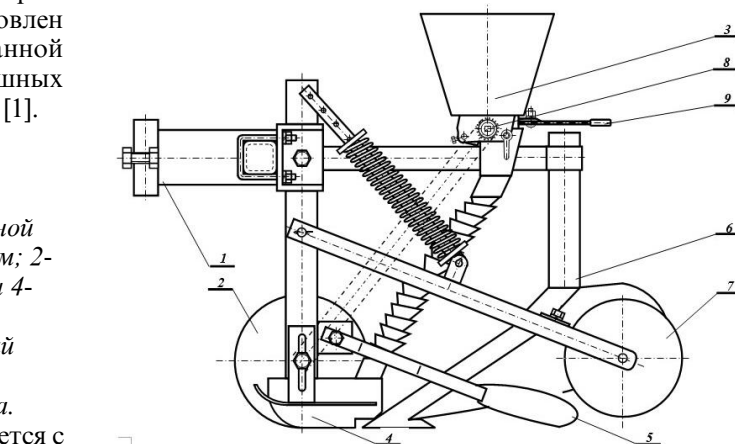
Конструктивная схема комбинированной малогабаритной 2-х рядной сеялки ТЗК-2: 1-рама с навесным механизмом; 2-опорно-приводное колесо; 3-ящик для семян 4-полозовидный сошник; 5-загортач; 6-бороздоделатель; 7-каток; 8- катушечный высевающий аппарат;
